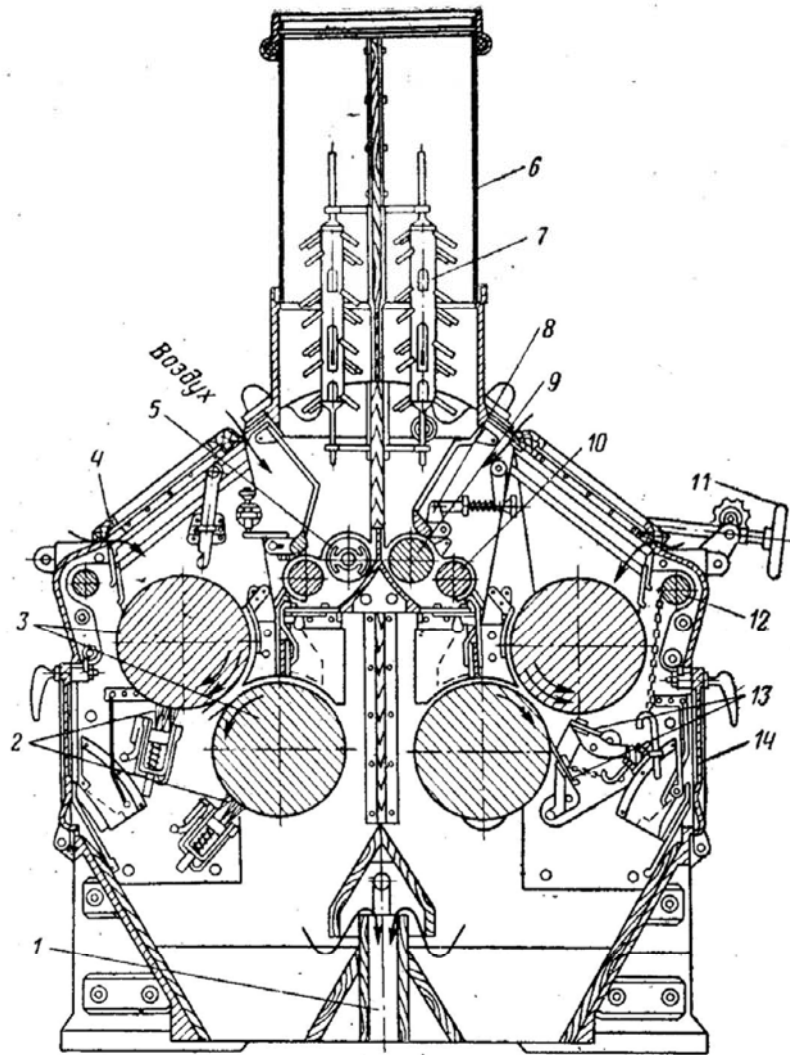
Схема вальцювого верстату типу ЗМ:
